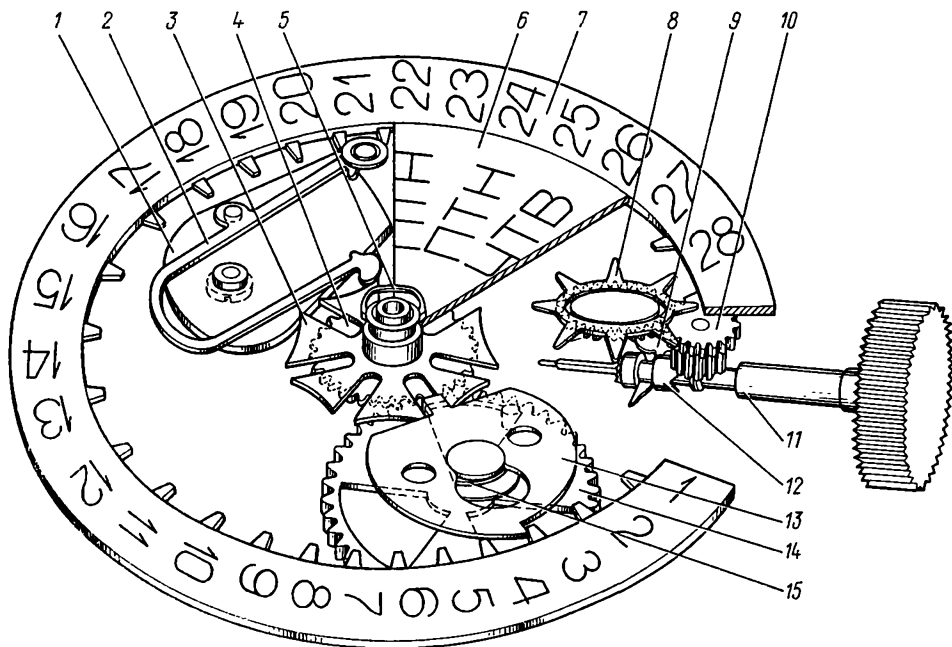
Кинематическая схема календарного устройства механизма часов 2350, 2360:
